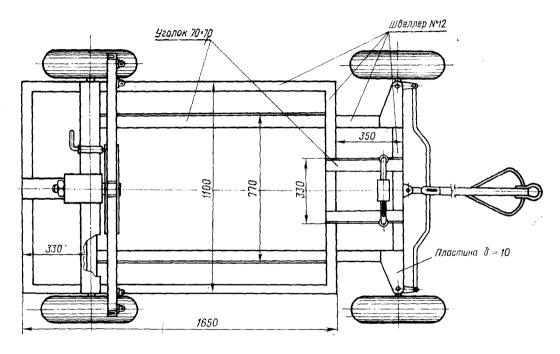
Тележка-стенд для ТО двигателя АШ-62ИР (вид сверху)
